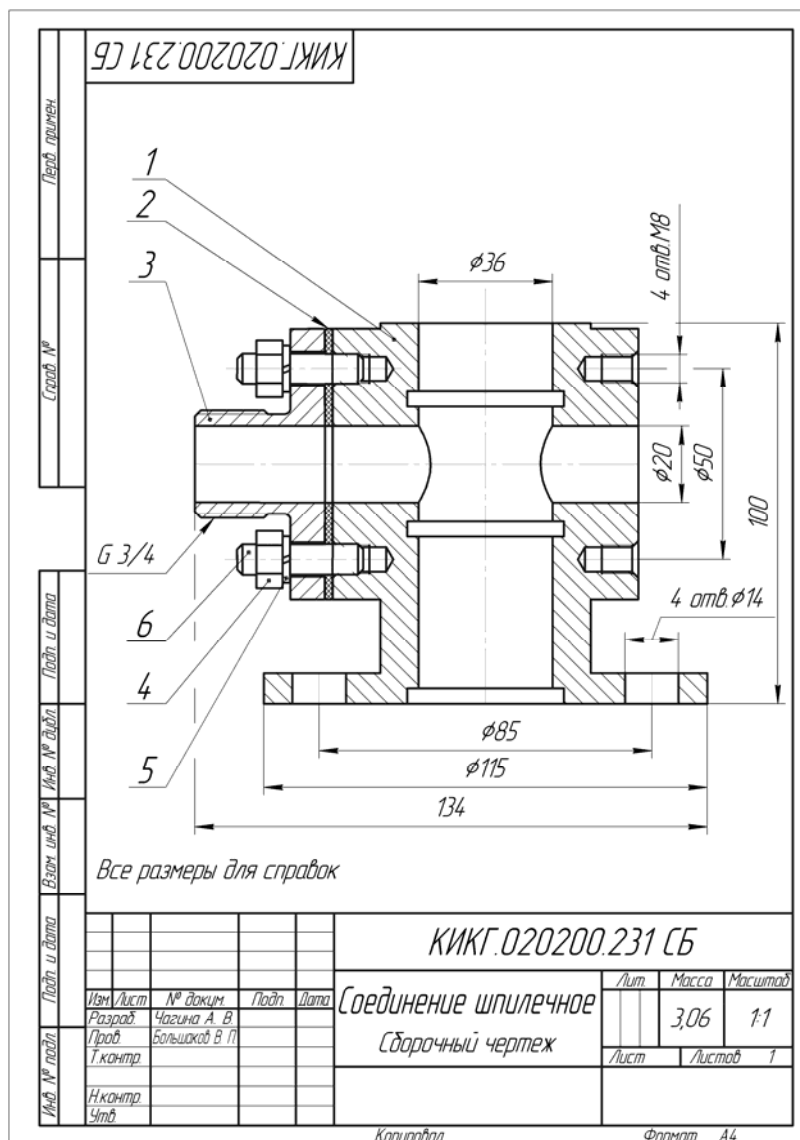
Ассоциативный сборочный чертеж соединения шпильчного
